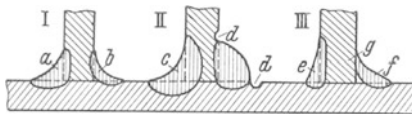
Schweißfehler bei Kehlnähten.
